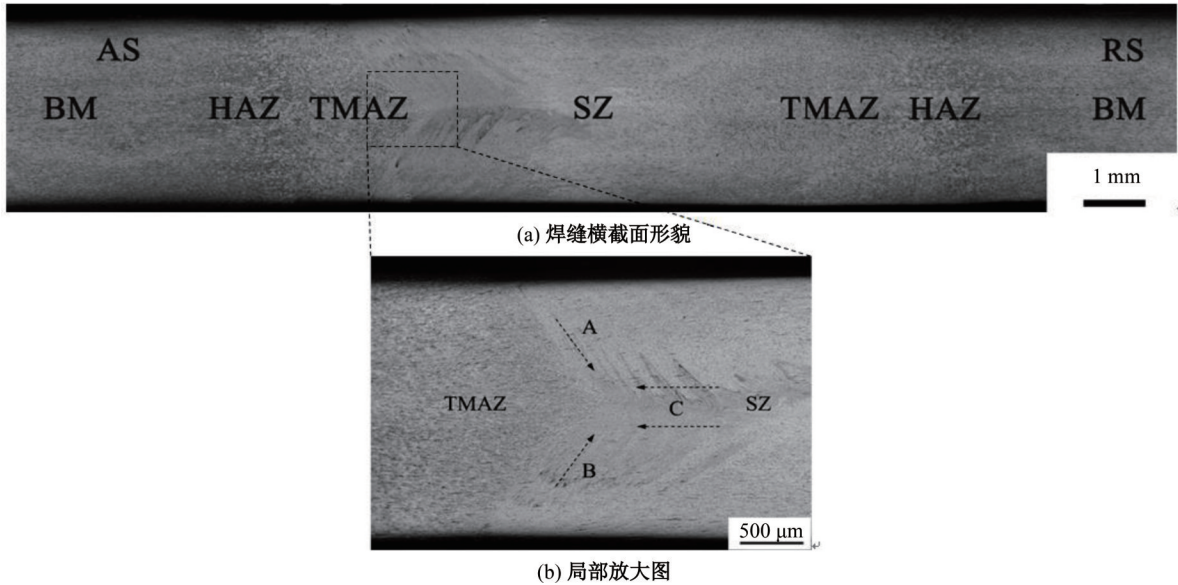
2024 铝合金 BT-FSW 焊接接头横截面形貌
